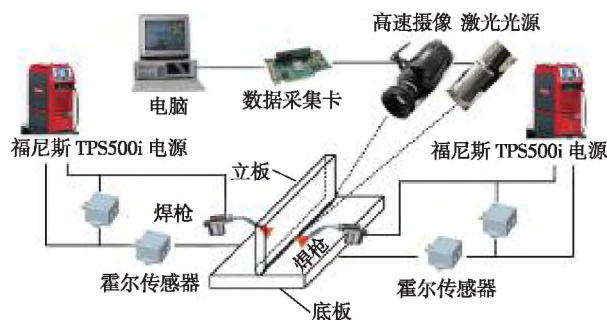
铝合金 T 形接头双侧脉冲 MIG 焊接系统
